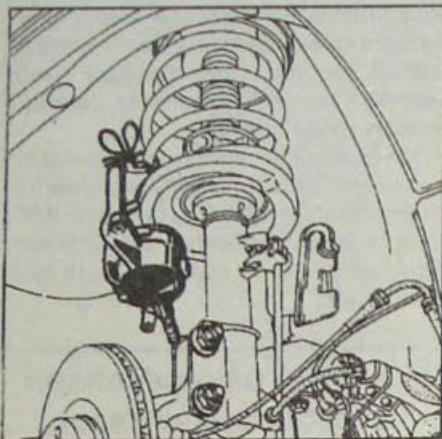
Крепление скобы суппорта тормозного механизма на пружине передней подвески
